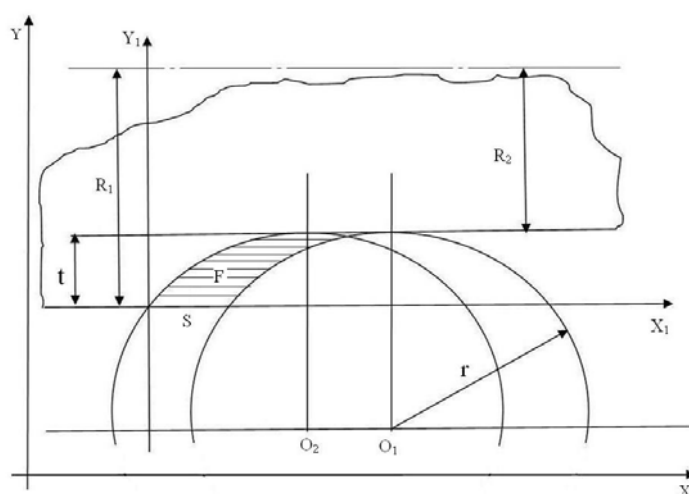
Схема снятия припуска резцом с круглой режущей пластиной на цилиндрической части заготовки
